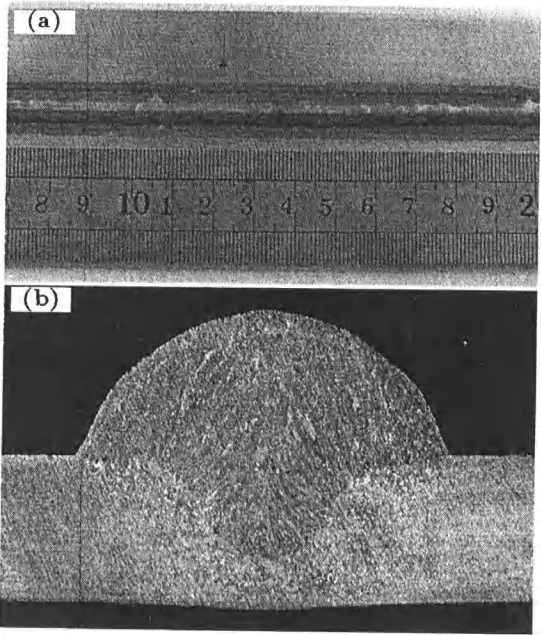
DE-GMAW 高速焊接的焊缝成形及焊缝横断面
